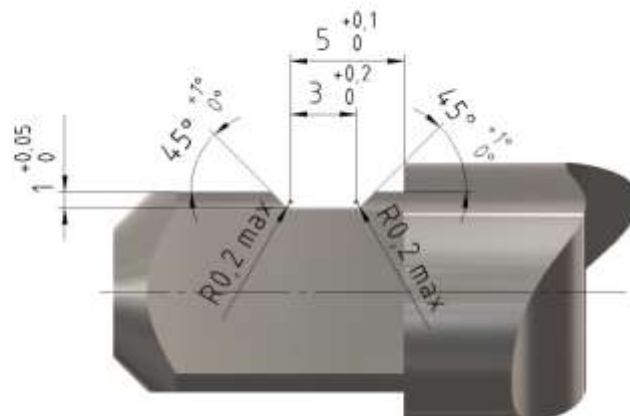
Maße der Nut für Gewindewerkzeuge mit Schaftdurchmesser 11,3 – 18 mm (Form B)
